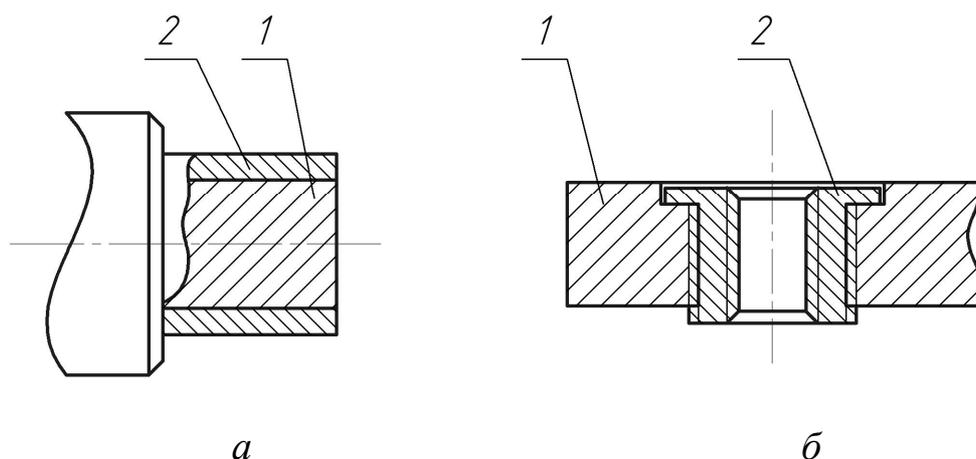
Восстановление изношенных шеек цапф (а), резьб (б) постановкой дополнительных деталей: 1 – изношенная деталь; 2 – дополнительная деталь
